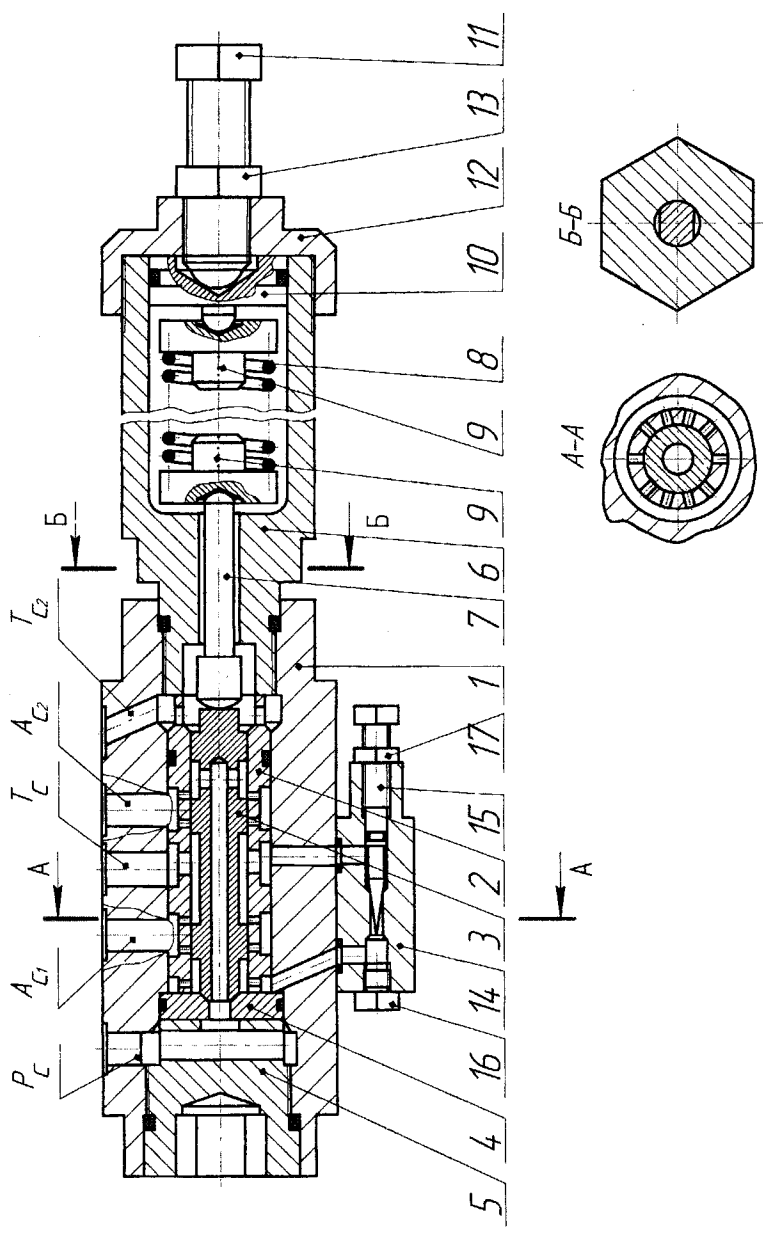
Конструкція сервопривода трилінійного двокаскадного швидкохідного ГТТ
